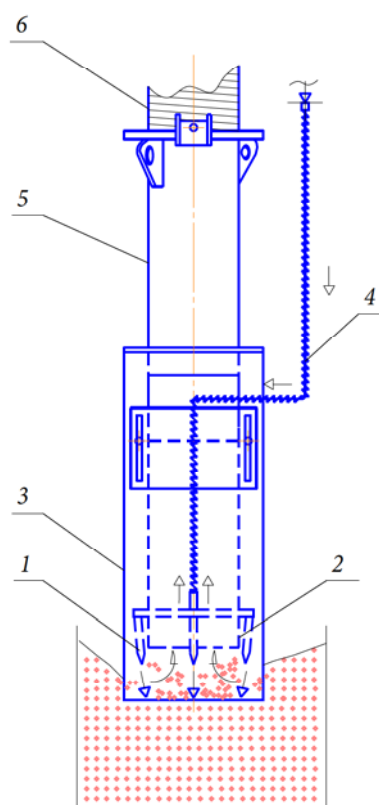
Модернизируемое заборное устройство всасывающей ПТУ: 1 — разрыхляющие сопла, установленные под углом к оси всасывающего наконечника; 2 — всасывающий наконечник; 3 — защитный кожух; 4 — нагнетательный трубопровод; 5 — корпус заборного сопла; 6 — всасывающий трубопровод
